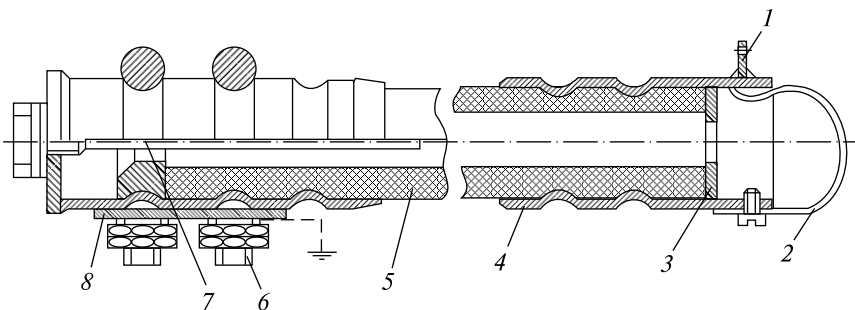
Трубчатый фибробакелитовый разрядник:
